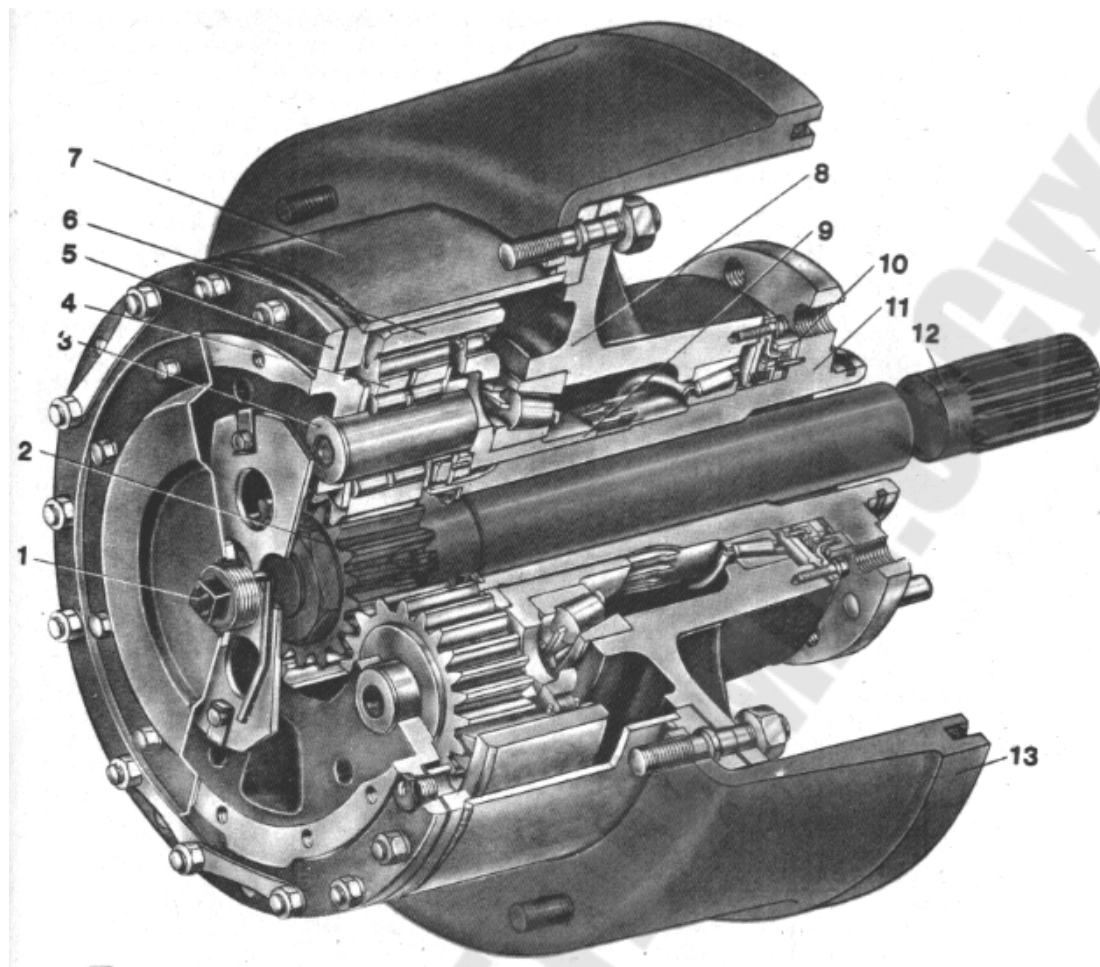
Колёсный редуктор трактора Т-150К:
